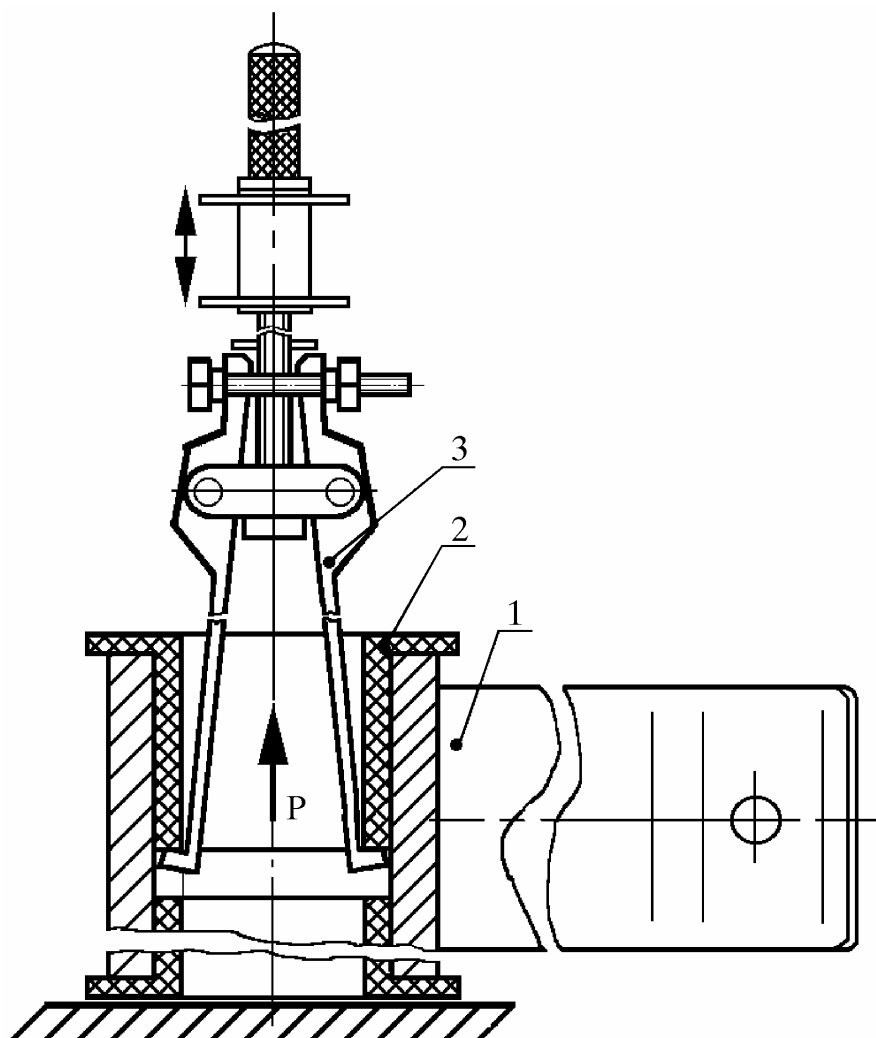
Выпрессовка втулок из корпуса опоры механизма управления:
